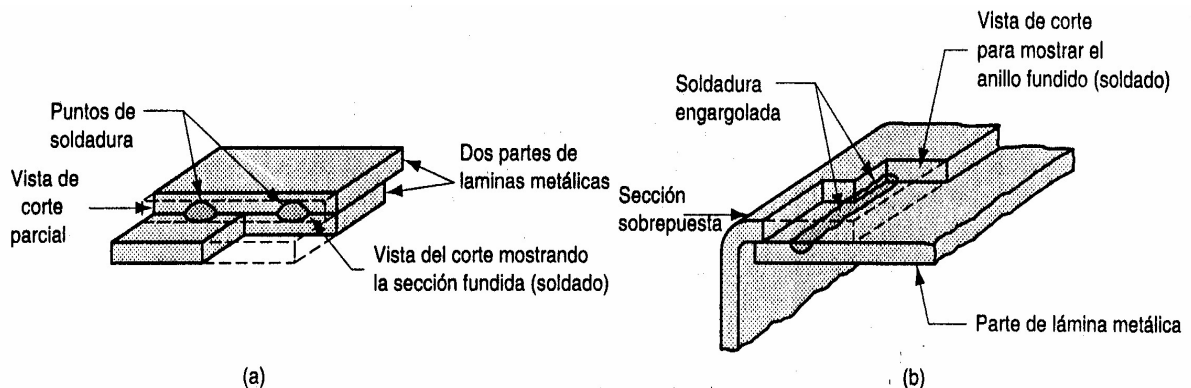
(a) Soldadura de puntos y (b) soldadura engargolada
